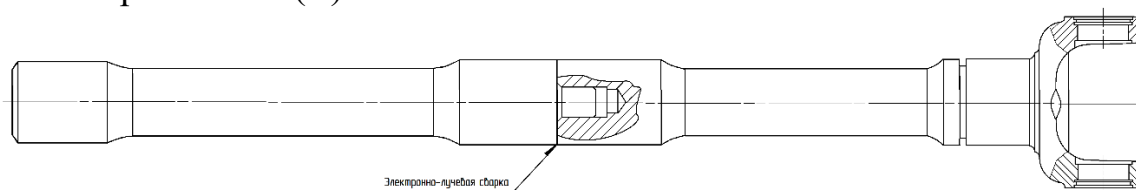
Эскиз внутреннего кулака новой конструкции
